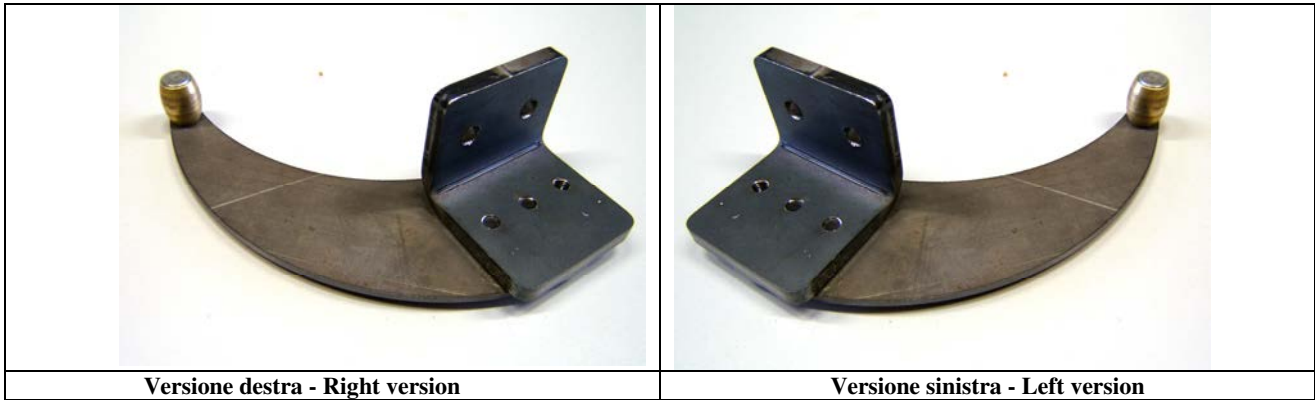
Esempio di montaggio della staffa con oliva - Example of a mounting bracket with roller
